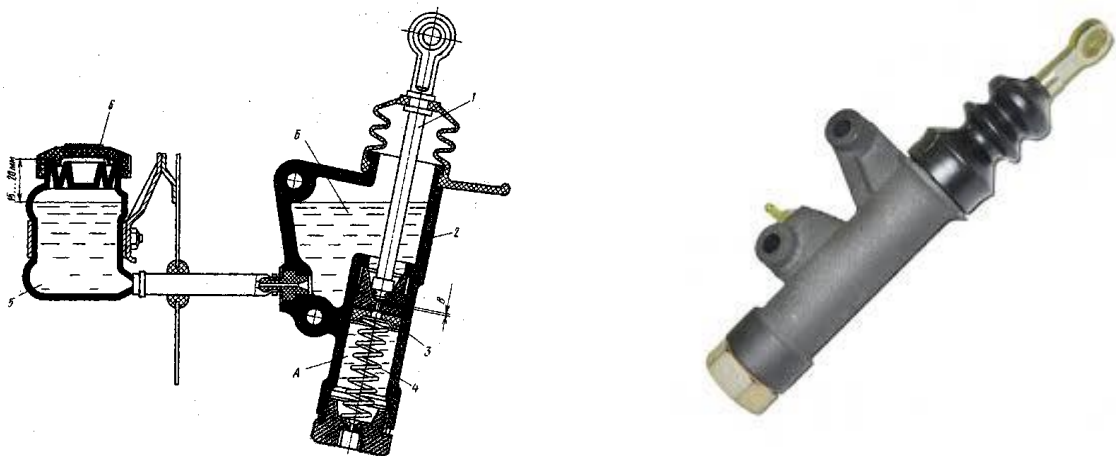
Головний циліндр зчеплення: 1 – штовхач; 2 – корпус; 3 – поршень; 4 – компенсаційний бачок; 5 – кришка бачка
